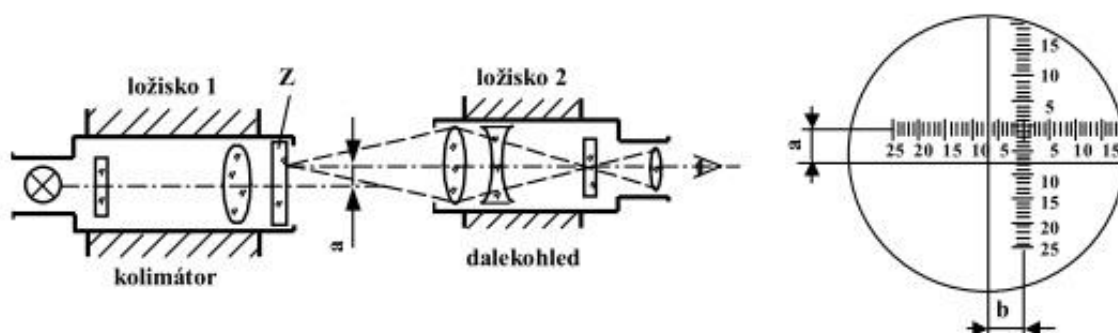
Souřadnicový měřicí přístroj pro měření polohy [20]
